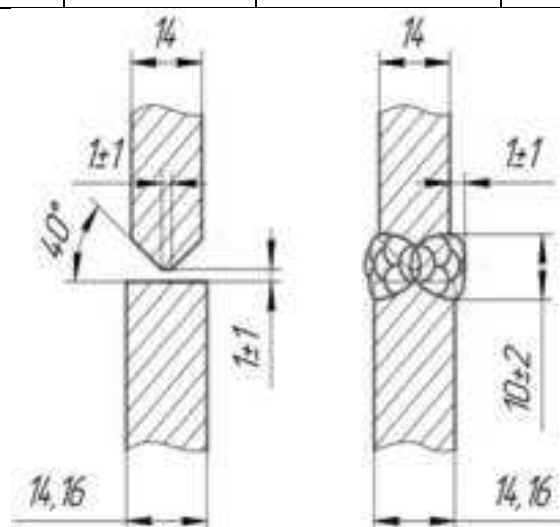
Разделка кромок и сварка горизонтальных соединений С15
